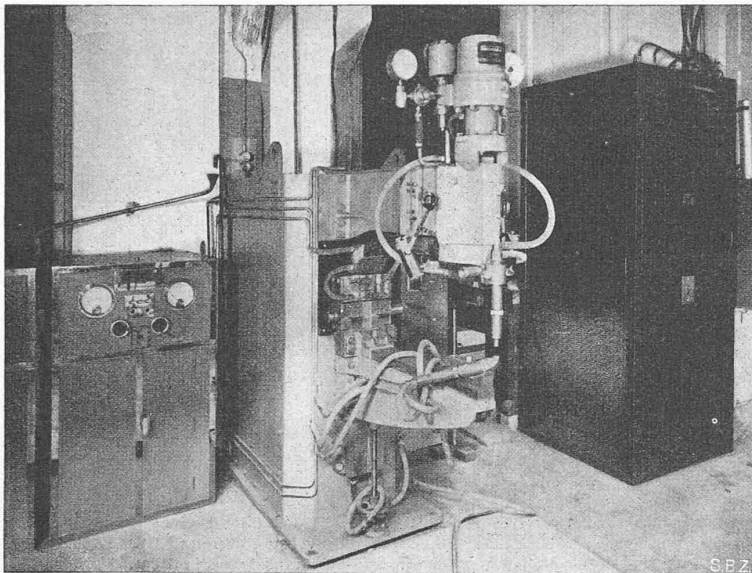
Sciaky-Punktschweissmaschine für Leichtmetall mit Kontrollapparat und Gleichrichter
